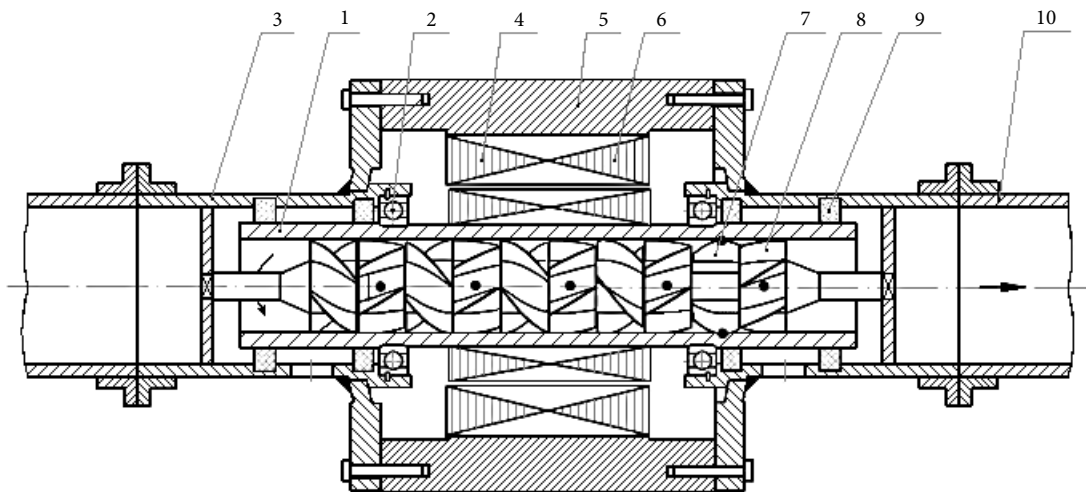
Многоступенчатый активатор закладочных смесей / Figure 6 | Multistage activator of stowage mixes. Активатор содержит вихревую камеру 1, установленную на подшипниках 2, внутри трубчатой проточной камеры 3. Электропривод вихревой камеры активатора имеет статорную электрообмотку 4, расположенную на внутренней поверхности корпуса 5, и роторную электрообмотку 6, закрепленную на наружной поверхности вихревой камеры. Внутри вихревой камеры проходит неподвижная ось, на которой установлены свободно сидящие втулки 7 с рабочими лопатками, присоединенными к вращающейся вихревой камере. Между этими втулками, на оси установлены неподвижные втулки 8 с лопатками, имеющими взаимно противоположный угол установки по отношению к рабочим лопаткам. Для герметизации подшипниковых опор от транспортируемой жидкости в проточной камере активатора установлены уплотнения 9. Активатор монтируется непосредственно на транспортный закладочный трубопровод 10.
